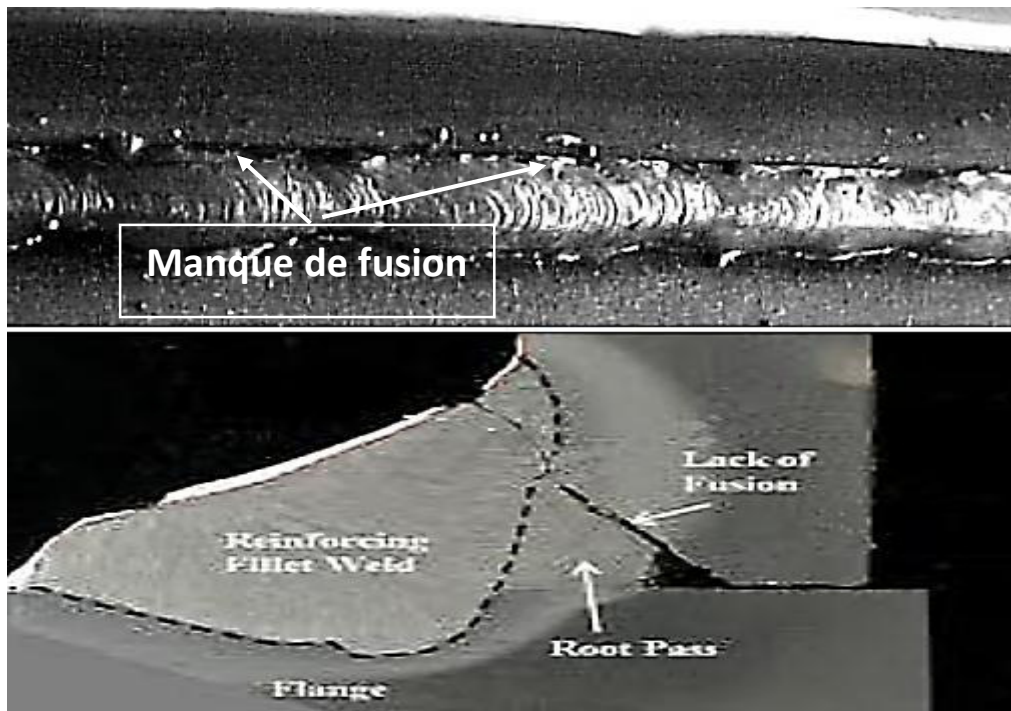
Manque de fusion à la racine de la soudure [31]
